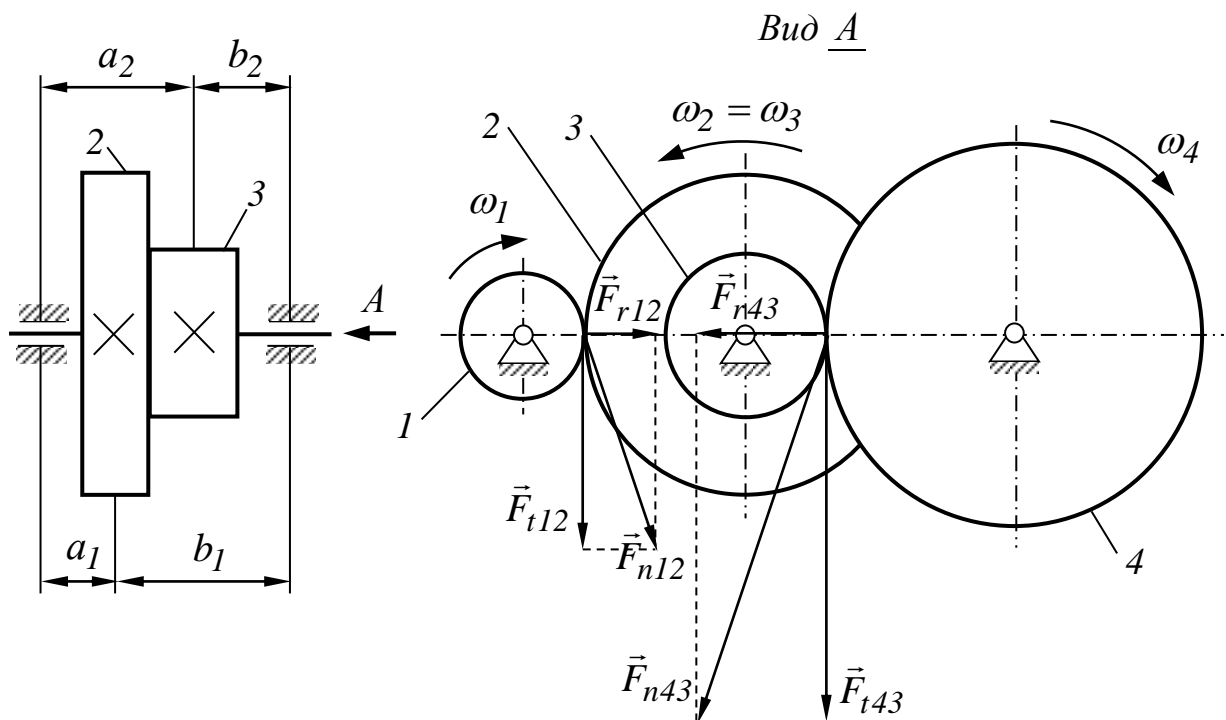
Схема проміжного вала та зусиль у зачепленні зубчатих коліс
